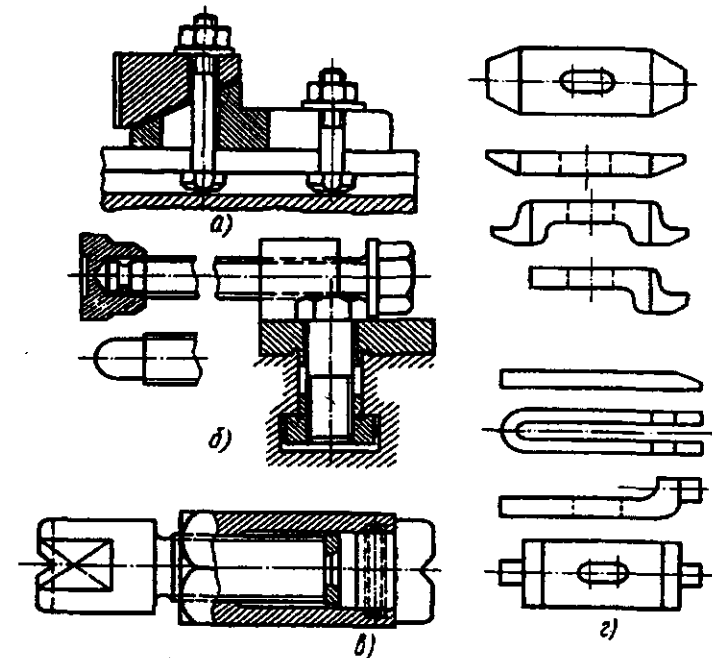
Принадлежности для крепления заготовок на расточных станках: а – прижим клиновой; б – прижим винтовой; в – распорный винт; г – прихваты
